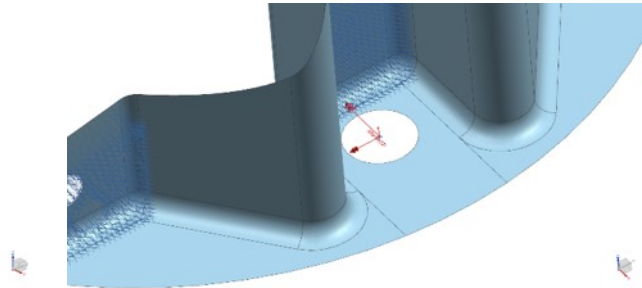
Ponto de aplicação do carregamento verificado na geometria final
